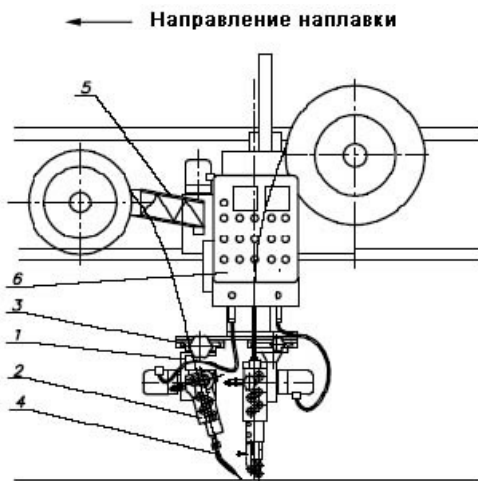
Сварочный автомат А-1416, доработанный для наплавки с присадкой: 1 – механизм подачи присадочной проволоки; 2 – правильный механизм; 3 – корректирующий суппорт; 4 – направляющий мундштук; 5 – кронштейн для кассеты; 6 – пульт управления
